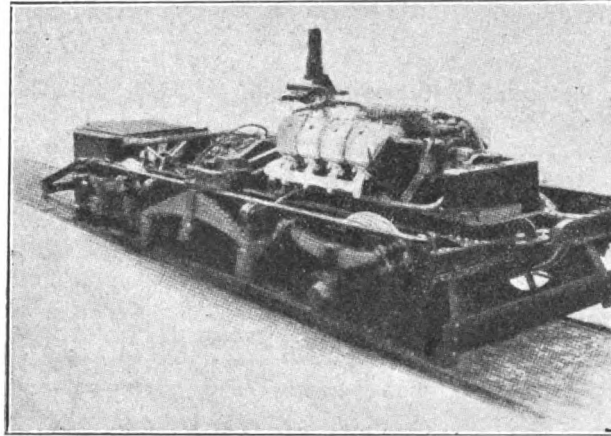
Motore Diesel con cilindri a V per automotrici della Simmeringer Waggonfabrik.
